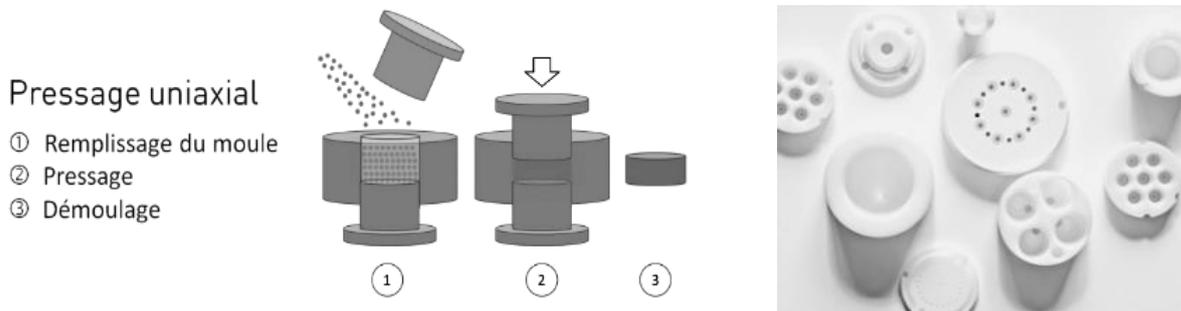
Etapes du procédé : Pressage-axial + Pièces de précision en céramiques techniques
